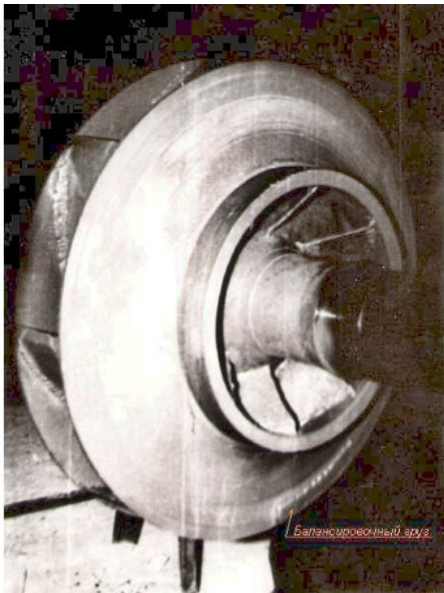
Рабочее колесо сварной конструкции для центробежного насоса 24НДс
